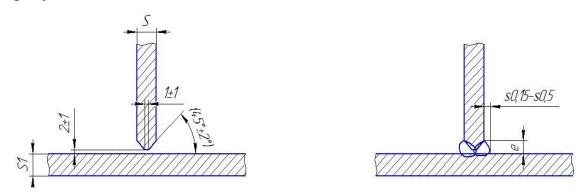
Конструктивные элементы сварного соединения
